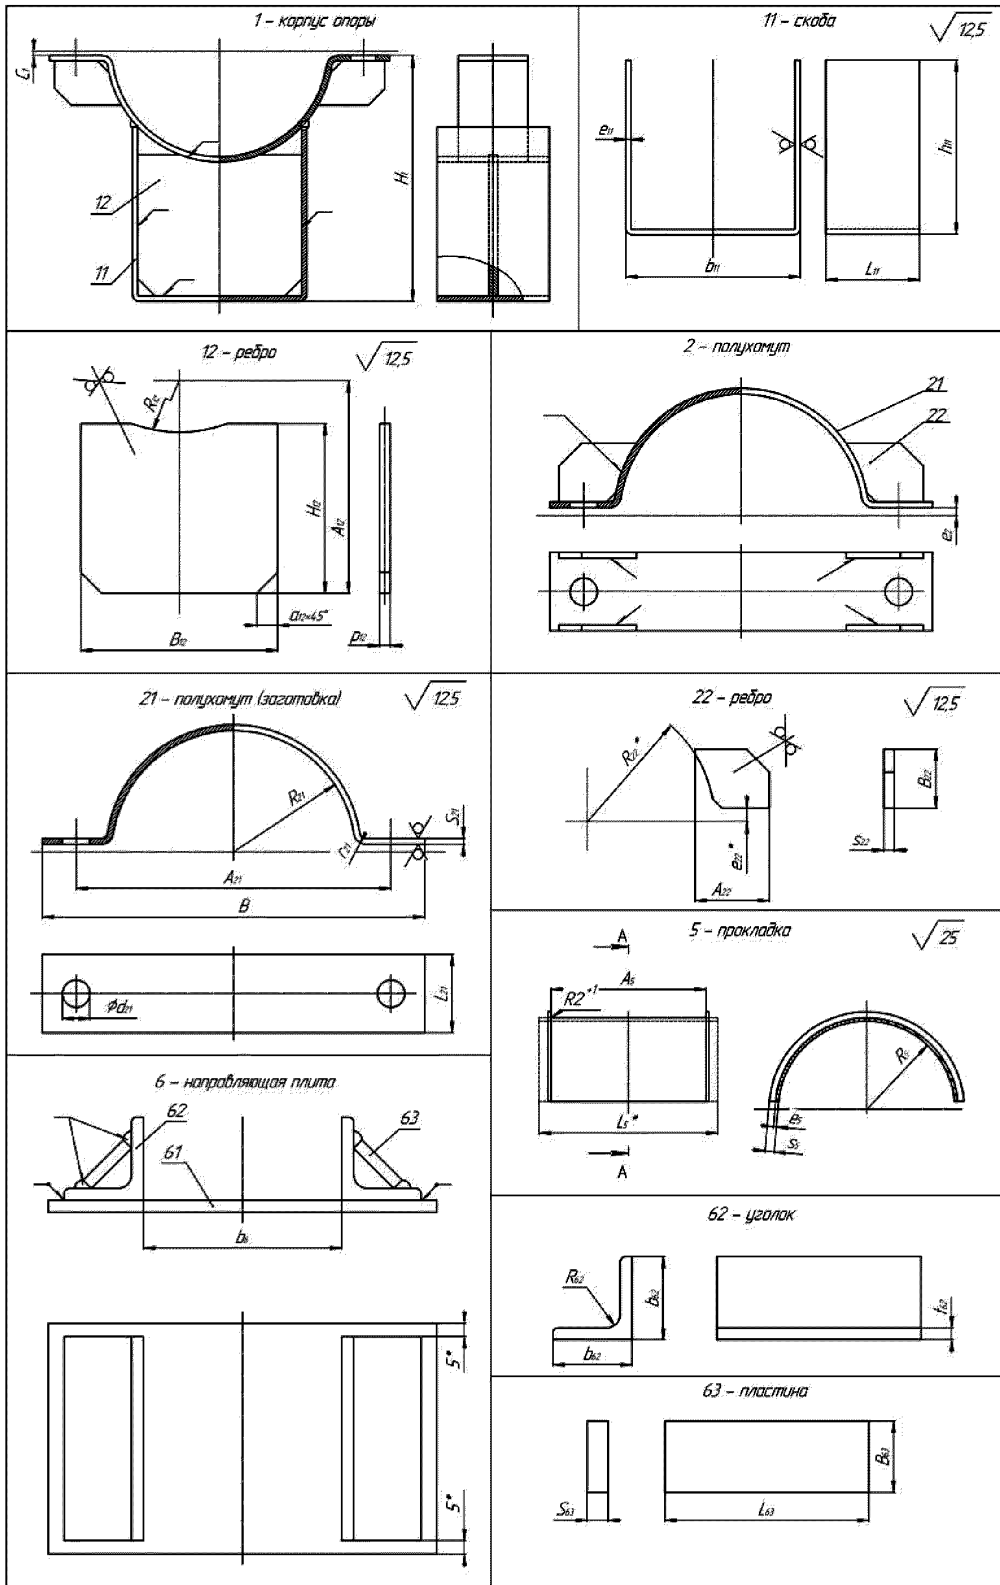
Детали изделий 01-XXXX-G-1C-02-B для
